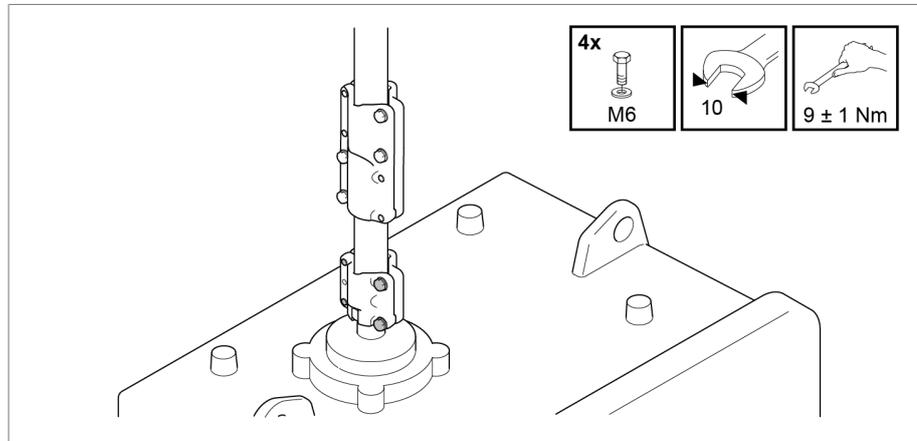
Fixer le tube carré sur le mécanisme d'entraînement
